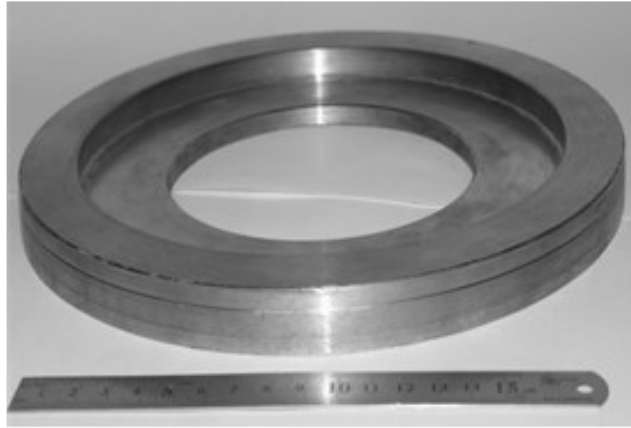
Внешний вид заготовки кольца разгрузки после взрывного плакирования и предварительной механической обработки
